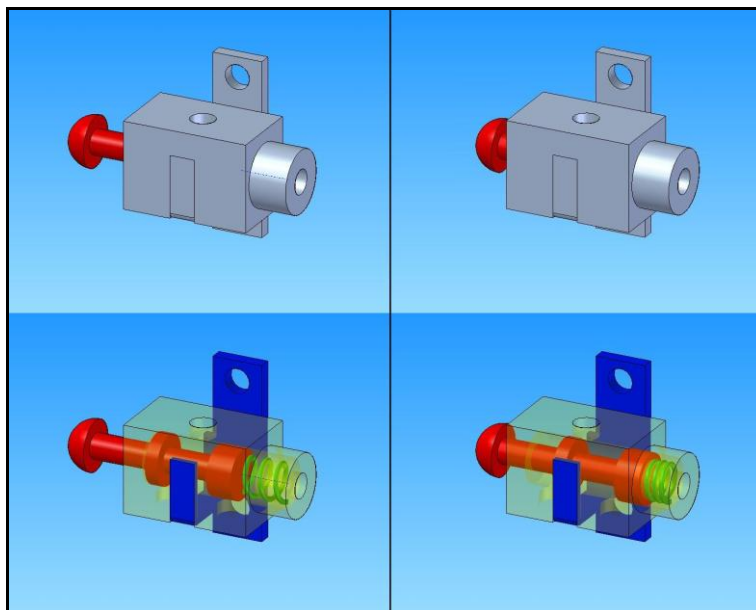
62 - Perspectivas de la válvula 3/2 sin accionar (izquierda) y accionada (derecha)
